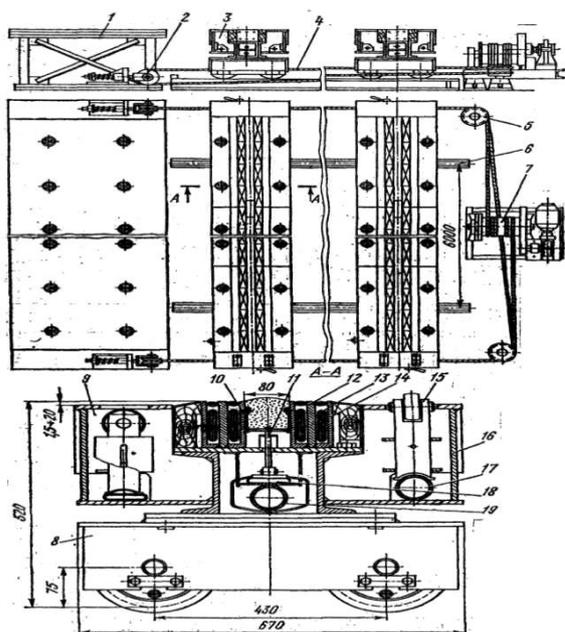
Электромагнитный стенд для сварки полотнищ
